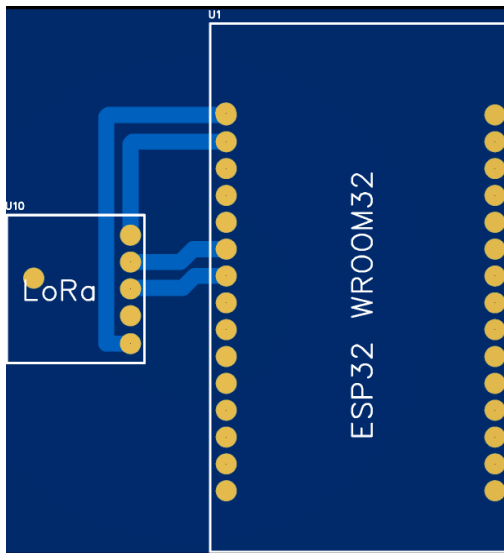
Vista previa del diseño final de PCB receptor en modo producción.
